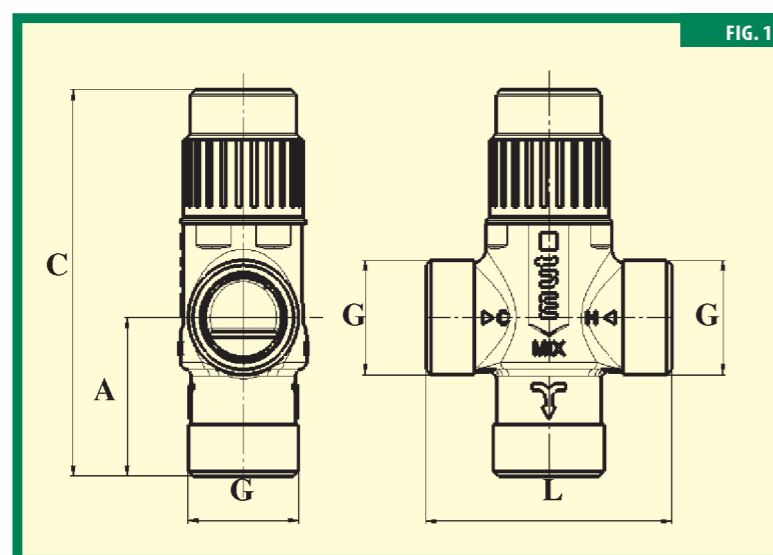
TWR-RA valve dimensions - Obr.1. Rozměry ventilu TWR-RA - Obr. 1. Rozměry ventilu TWR-RA
